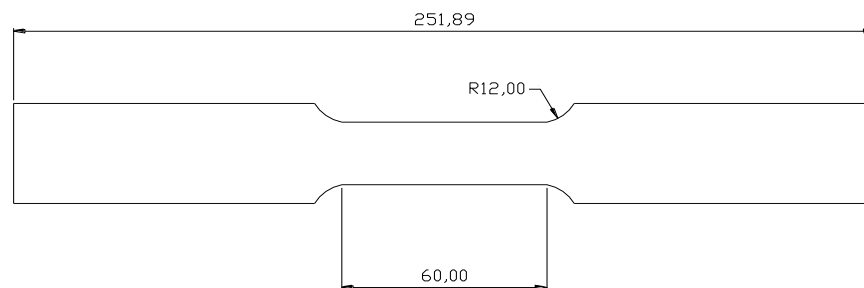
Dimensiones de probetas para el ensayo de tracción en junta soldada.
